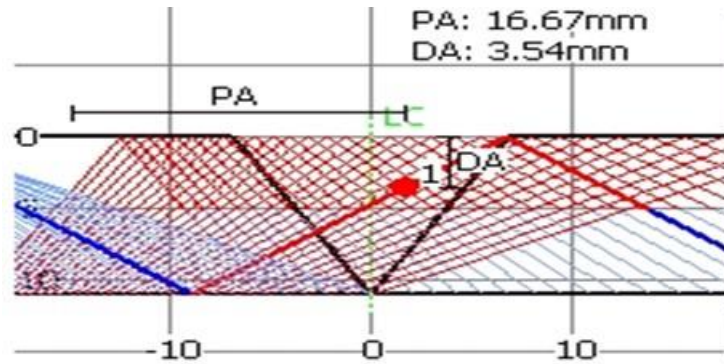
Tubería de inspección de soldadura punto 1.
